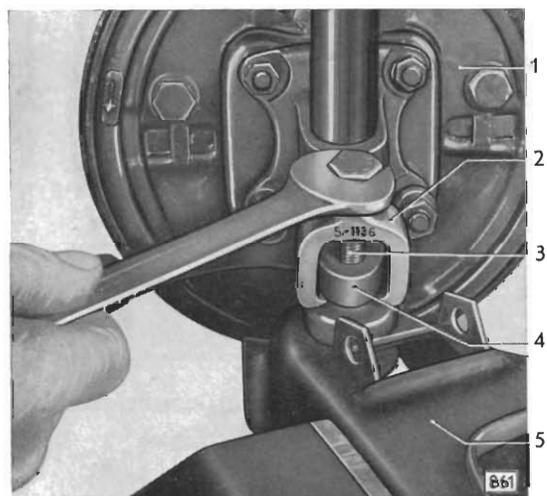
Kugelbolzen mit Kugelbolzen-Abzieher S-1136 aus Achsschenkel drücken
